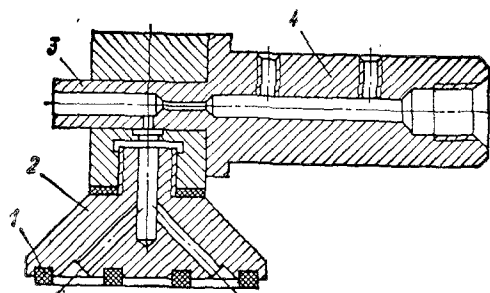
Вакуумное захватное устройство промышленного робота МП-9С для плоских деталей
